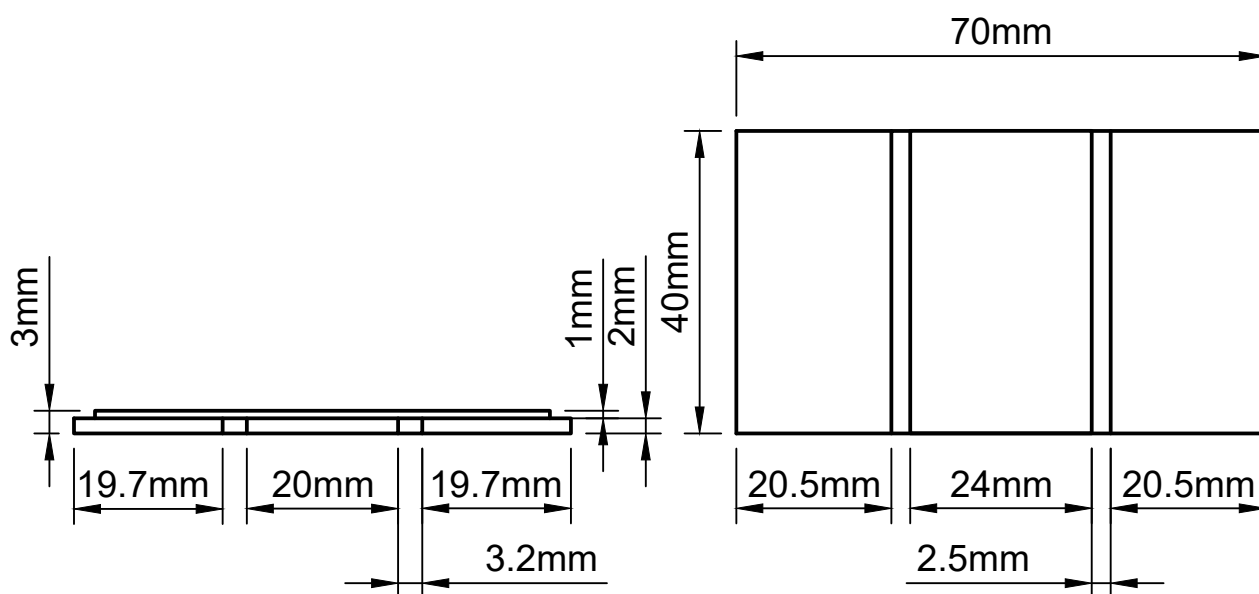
Pouzdro kolorimetru, pohled ze shora
